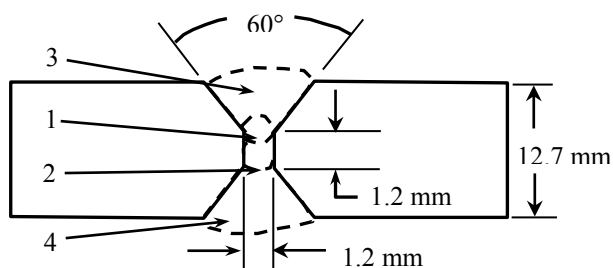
Diseño de unión para soldar el acero inoxidable dúplex 2205.
